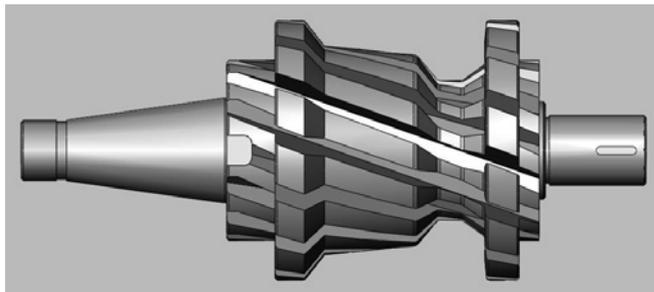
Модель корпуса фасонной фрезы с пазами под ножи
